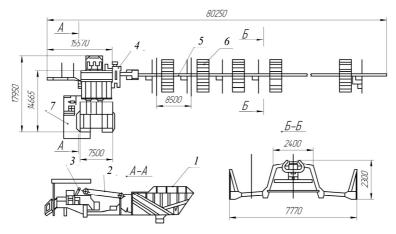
Линия сортировки бревен ЛСБ-15: 1 – разобщитель пачек бревен ЛТ-80A или РБ-100; 2 – поперечный конвейер; 3 – шиберное устрйство; 4 – измеритель диаметров бревен; 5 – сортировочный конвейер; 6 – накопители бревен; 7 – кабина оператора
